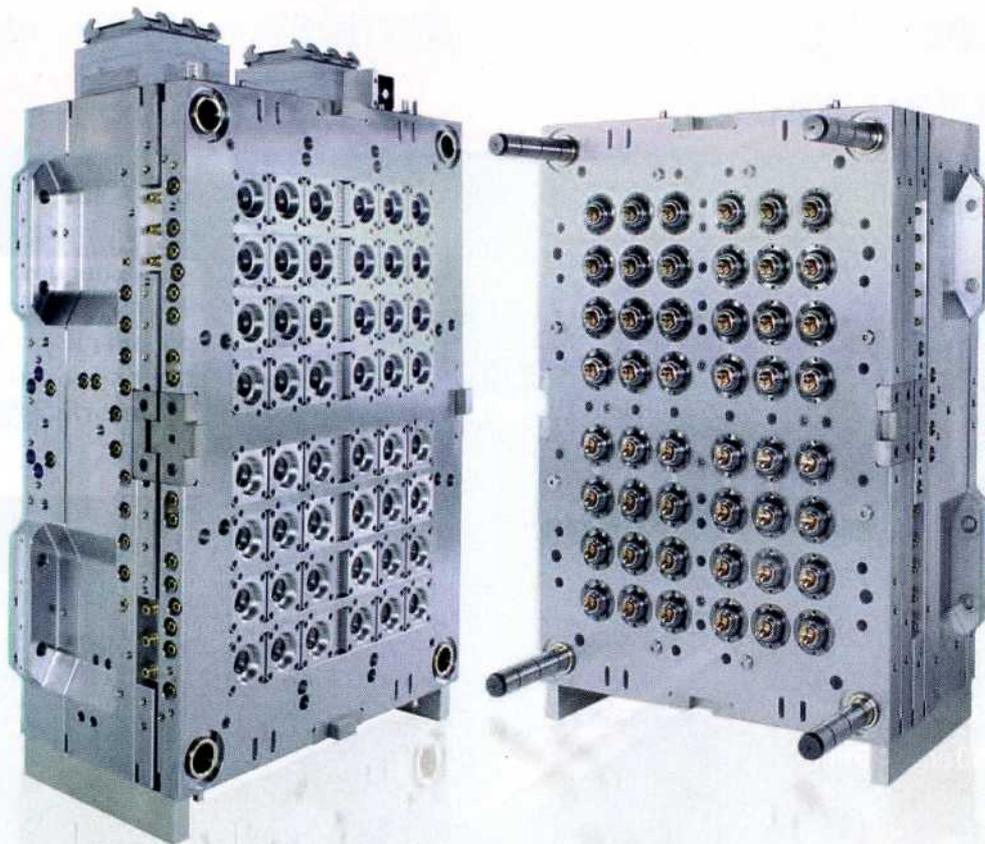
Männer fertigt Mehrfachwerkzeuge mit bis zu 128 Kavitäten
